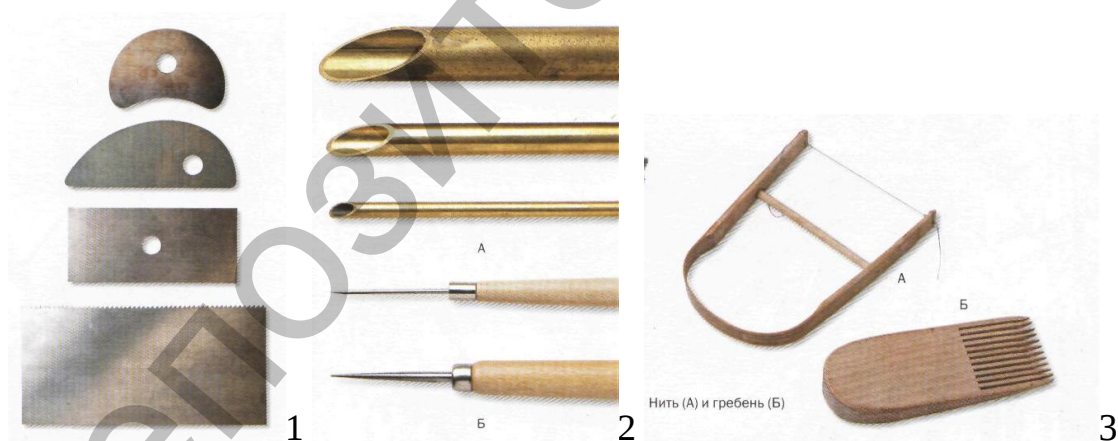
Инструменты и приспособления для формования на гончарном круге:
